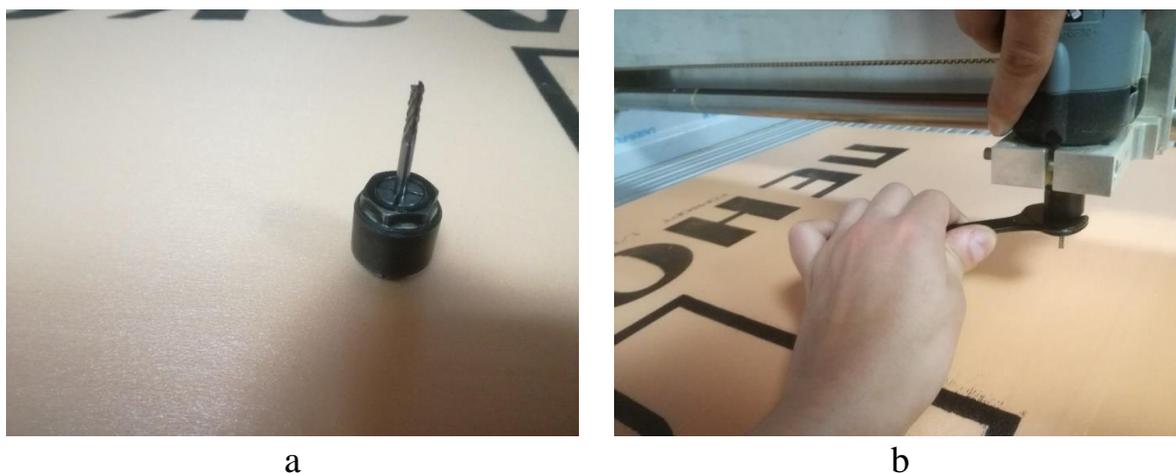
Финальная сборка фреза-цанга-гайка (а) и установка фрезы в шпиндель (b).
